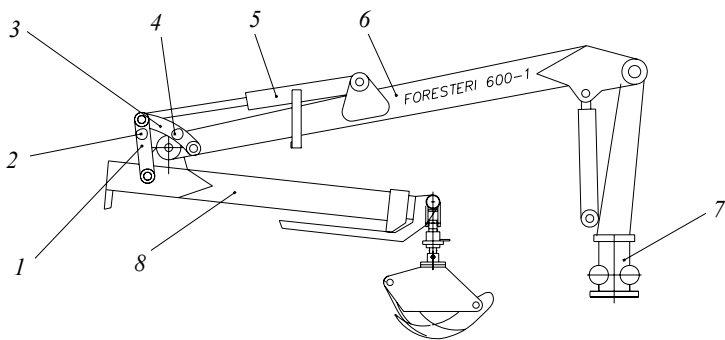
Гидроманипулятор форвардера «Амкодор 2661-01»: 1–4 – тяги; 5 – гидросистема; 6 – стрела; 7 – поворотное устройство; 8 – рукоять
